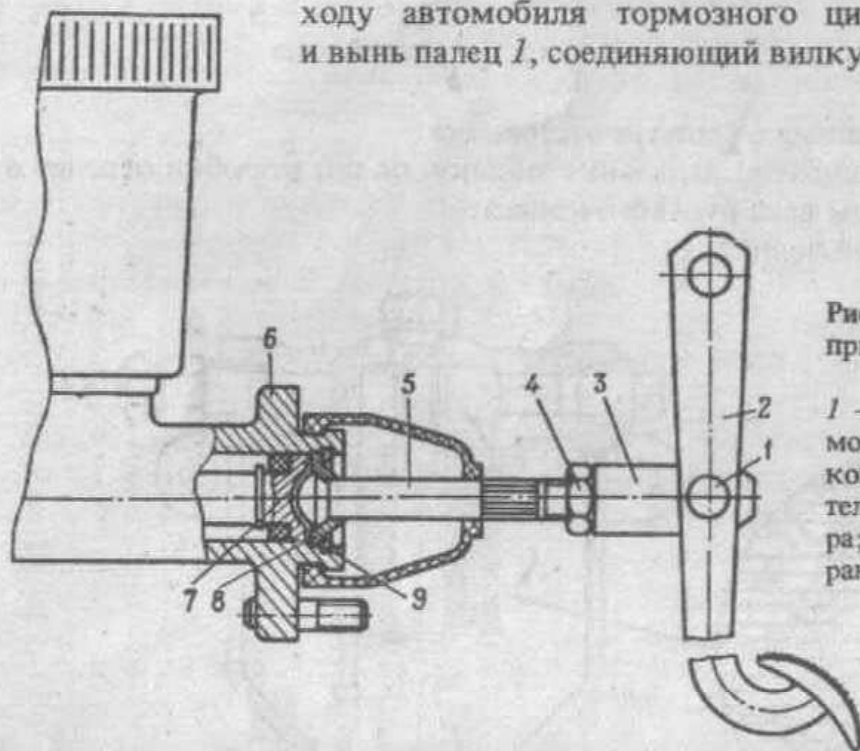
Узел регулировки привода главных тормозных цилиндров:
